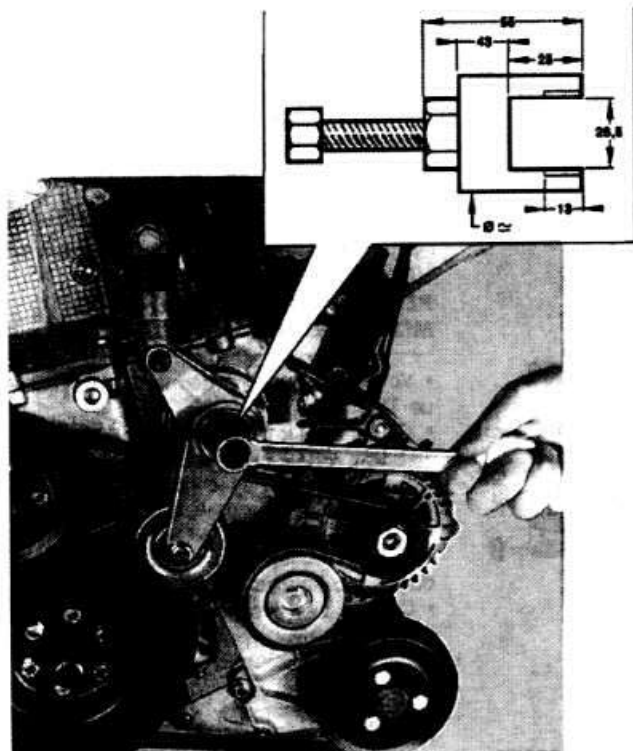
Приспособление BMW 13.5.120 для спрессовки корпуса ТНВД
